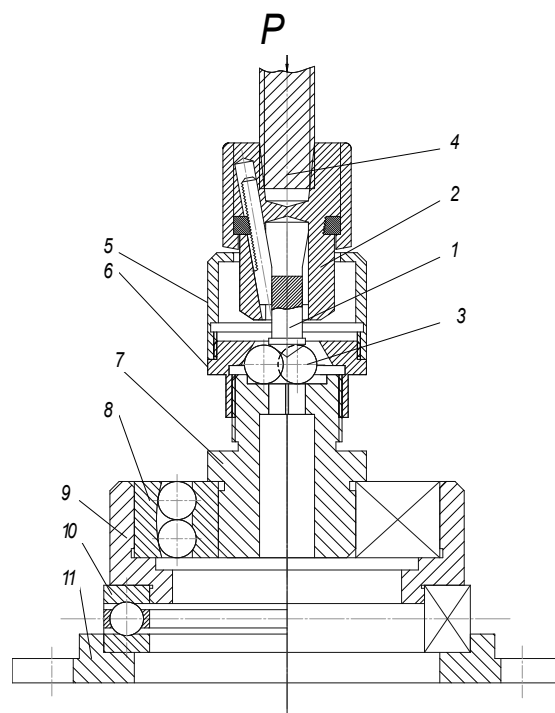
Робочий вузол установки для чотирикулькової схеми
